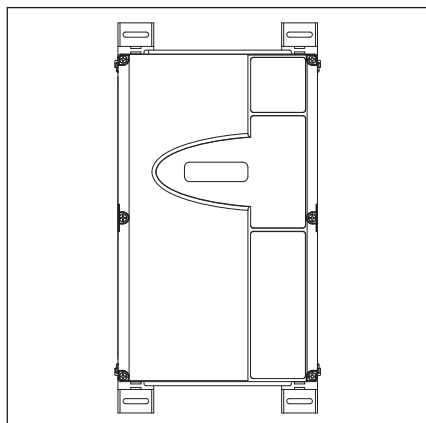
Корпус блока управления с вертикально закрепленными монтажными опорами
